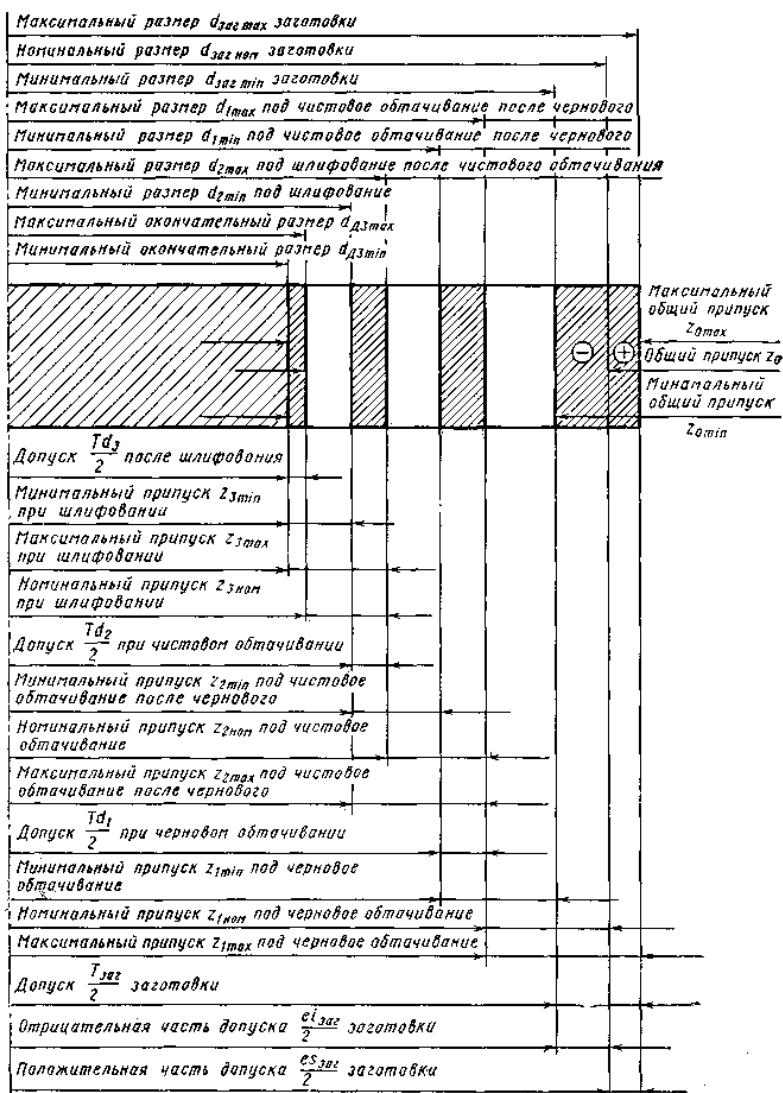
Схема расположения припусков, допусков и предельных размеров на обработку поверхности вала
